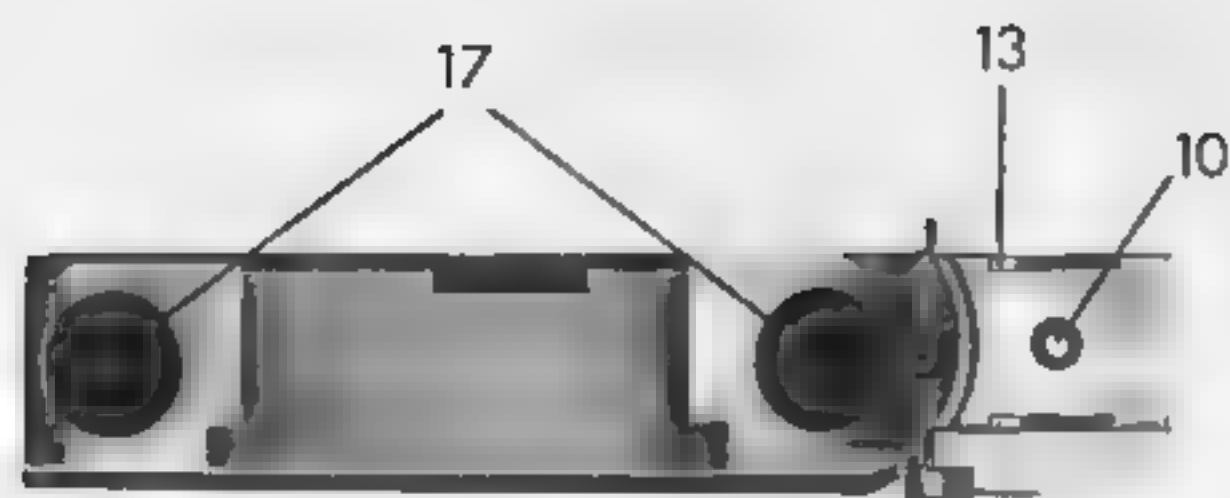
Das Querstück von vorn gesehen: 10 = Schlagbolzen, 13 = Auswerfer, 17 = die Lager für die Federn (14)
